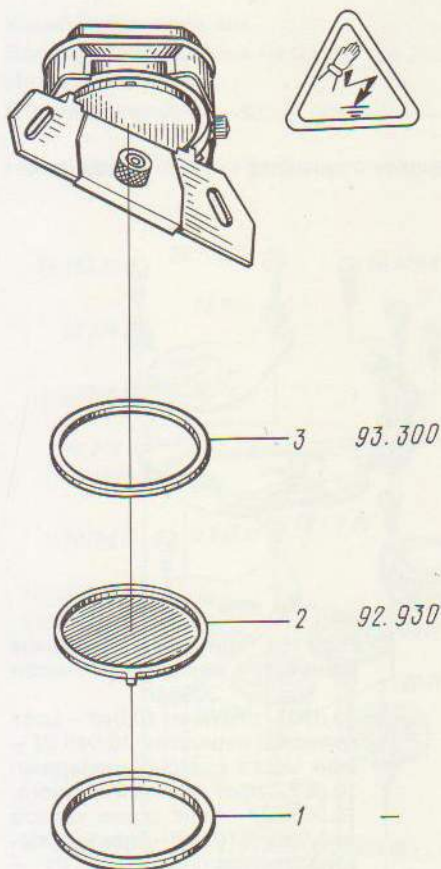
1 – кольцо крепления крышки; 2 – крышка (дно); 3 – прокладка корпуса
